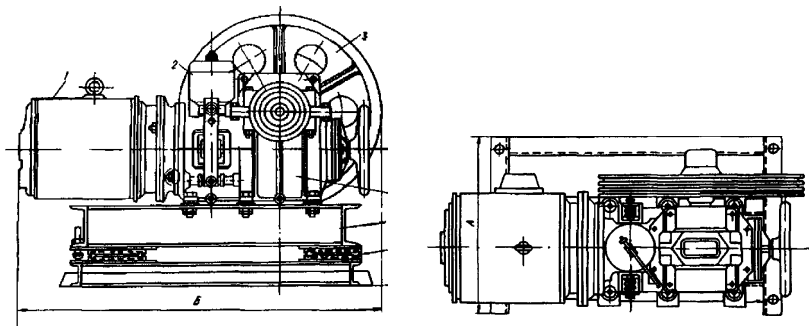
Лебедка лифтовая редукторная ЛП-160, ЛП-180
